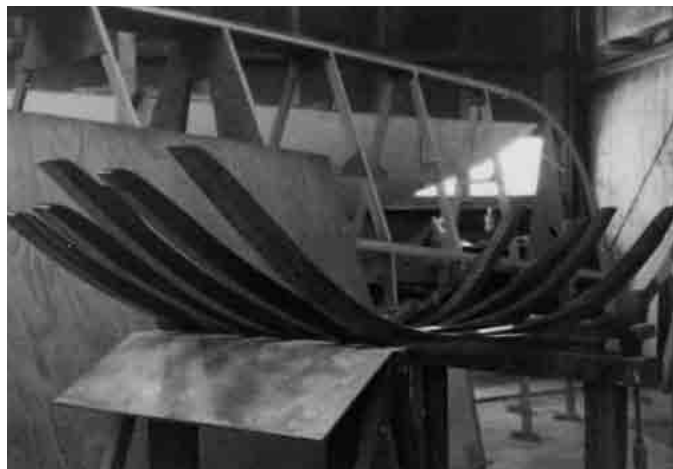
Lamellierte Bodenwangen, zugepaßt und beschichtet, fertig für den Einbau.
